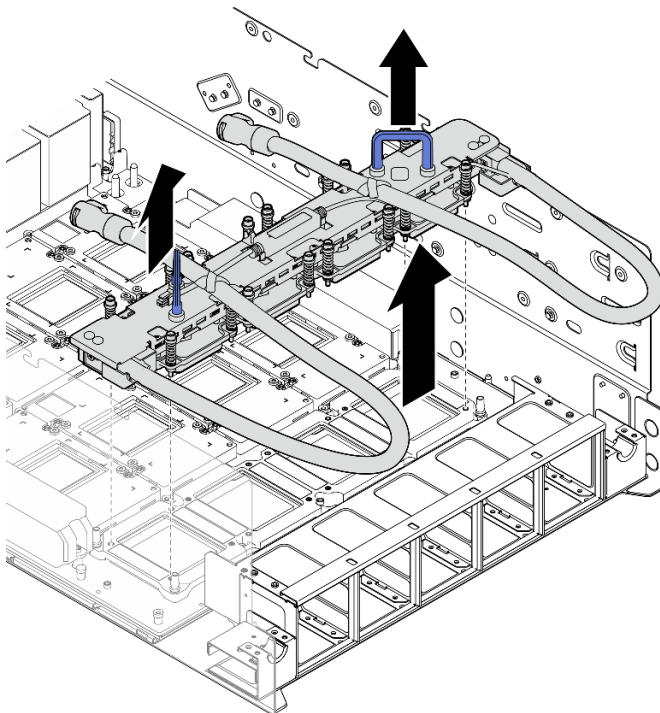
Entfernen des NVSwitch-Kühlplattenmoduls
